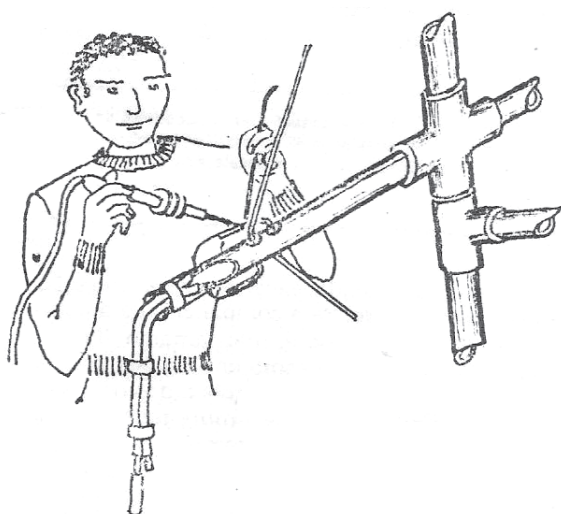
Soldando o balun e o cabo coaxial ao elemento irradiante (é preciso soldar por causa da chuva!).
